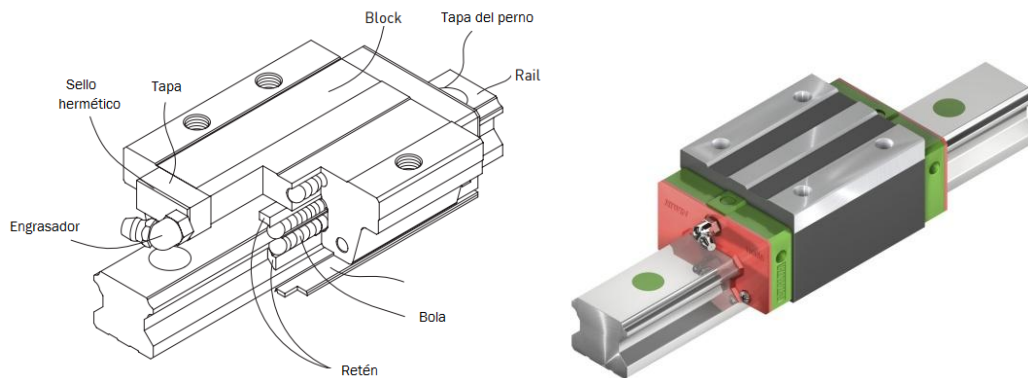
Sección del carro deslizante montado sobre el raíl (izq.) e imagen real del carro (dcha.).⁷
